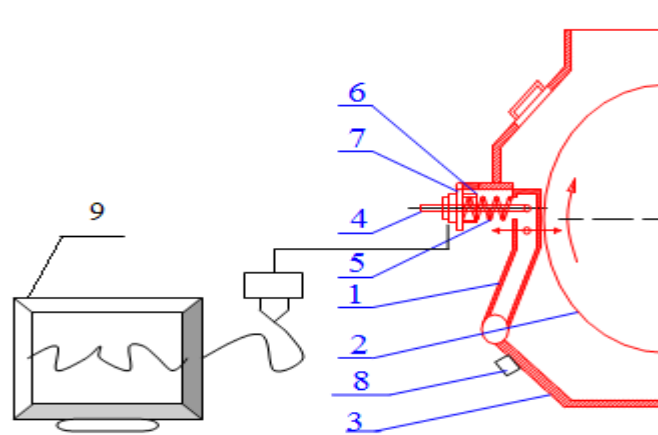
Пластикатор: 1 – каркас; 2 – барабан; 3 – корпус машини; 4 – шарнірно-рухомий гвинт; 5 – пружина; 6 – регуляторний пристрій; 7 – гайка; 8 – термодавач; 9 – монітор
